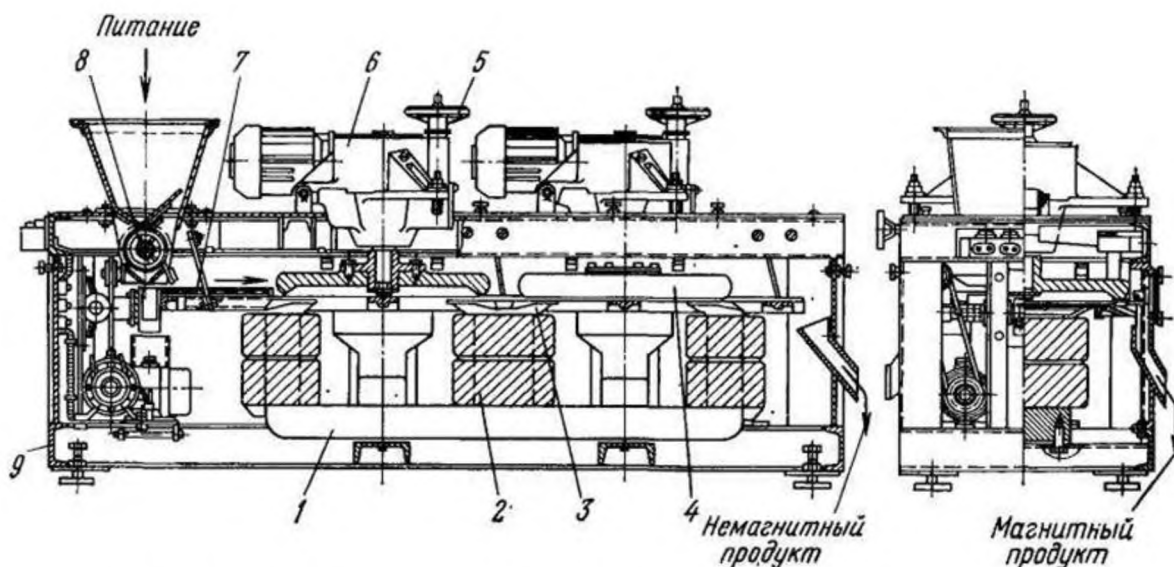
Электромагнитный дисковый сепаратор МС-2: 1 — электромагнитная система; 2 — обмотка; 3 — сердечники и полюсные наконечники; 4 — стальные диски; 5 — штурвалы для регулирования рабочих зазоров; 6 — приводы дисков; 7 — вибрационный лоток; 8 — барабанный питатель; 9 — рама
